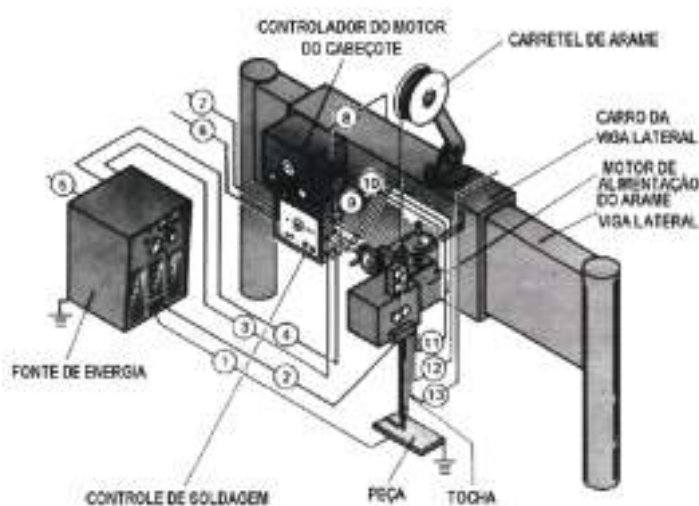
Instalações para a soldadura automática (mecanizada): 1. Cabo
